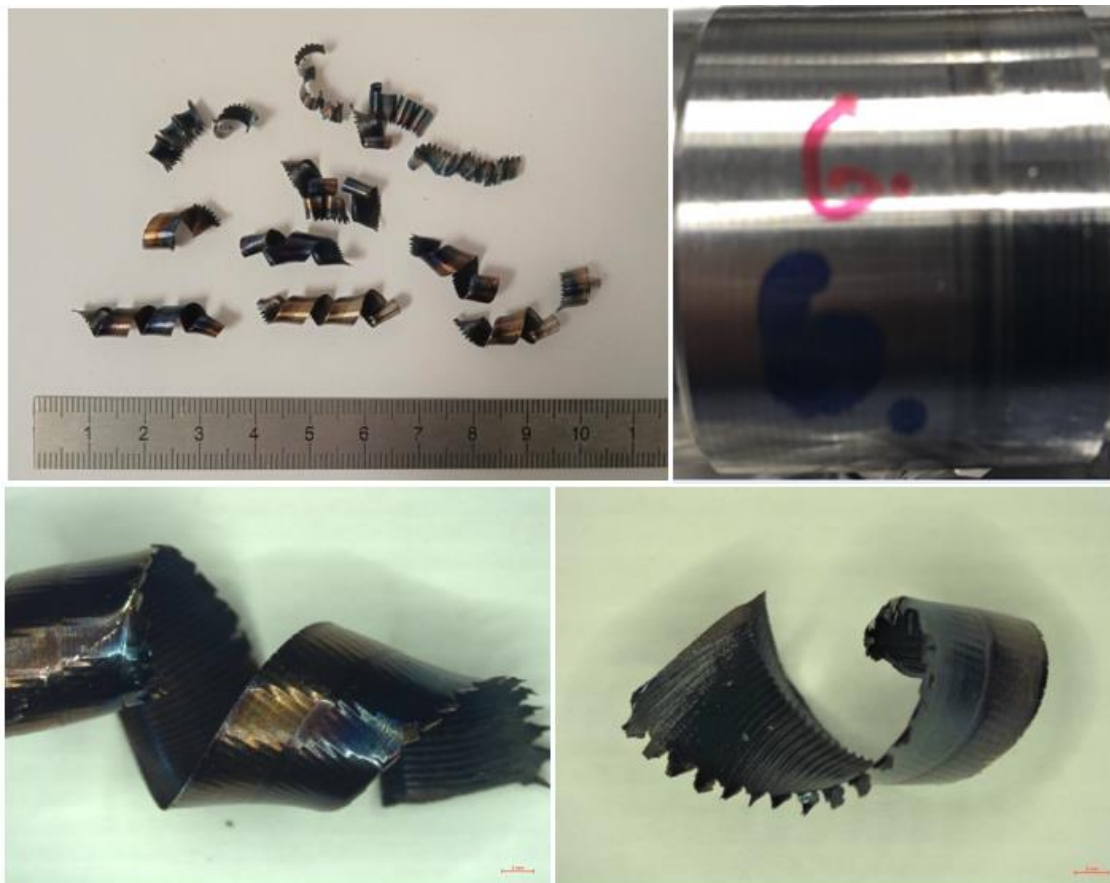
Třísky a obrobený povrch, VBD 3
